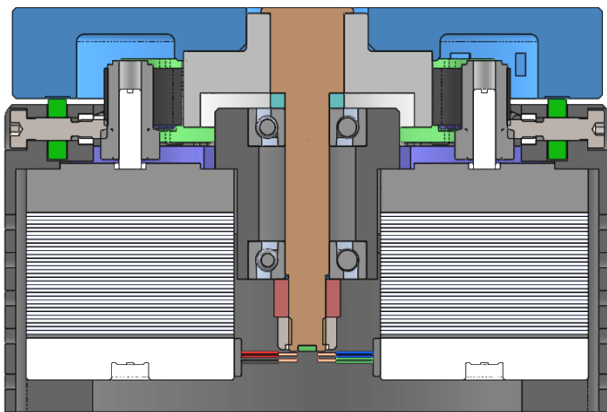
Původní verze 1. osy robotu BCN3D MOVEO
